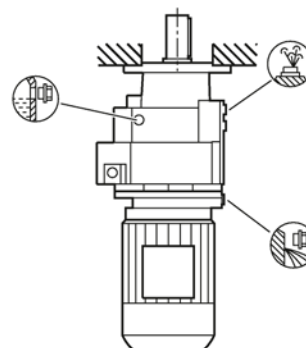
Монтажные положения для цилиндрического редуктора DF/ZF в исполнении с фланцем и DZ/ZZ с фланцем корпуса, типоразмеры 19–29
